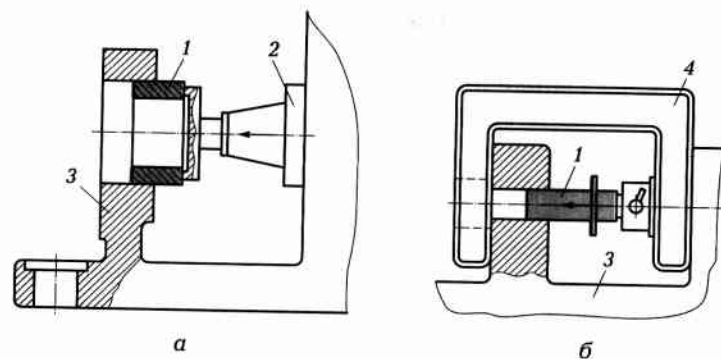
Оборудование для запрессовки: а — винтовой домкрат; б — гидравлическое приспособление; 1 — запрессовываемая деталь; 2 — винтовой домкрат; 3 — корпусная деталь; 4 — гидравлическое приспособление (скоба)
